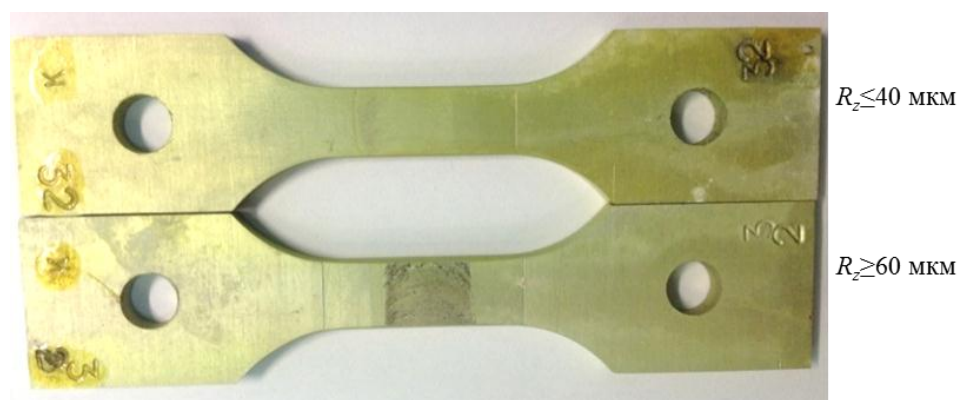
Внешний вид сварных образцов с различной шероховатостью поверхности с анодно-оксидными покрытиями после испытаний в КСТ
